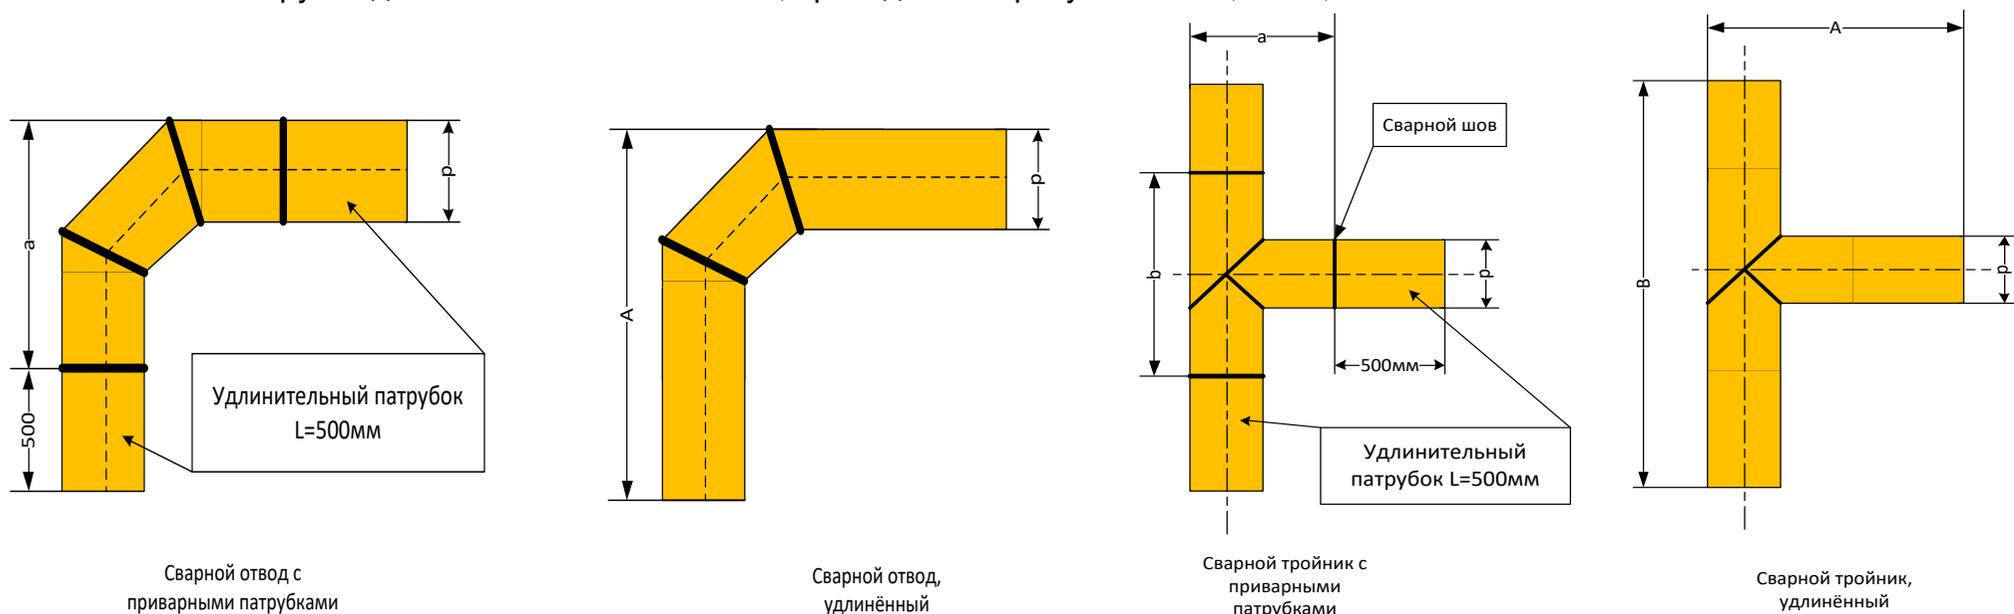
Варианты исполнения соединений полиэтиленовых труб и фитингов (Сварной отвод с приваренным патрубком)
